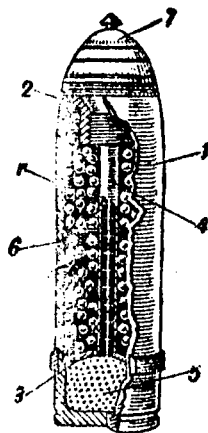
Шрапнель: 1 — корпус шрапнели (стакан); 2 — головка; 3 — перегородка; 4 — центральная трубка; 5 — вышибной заряд (дымный порох); 6 — пули; 7 — дистанционная трубка.
